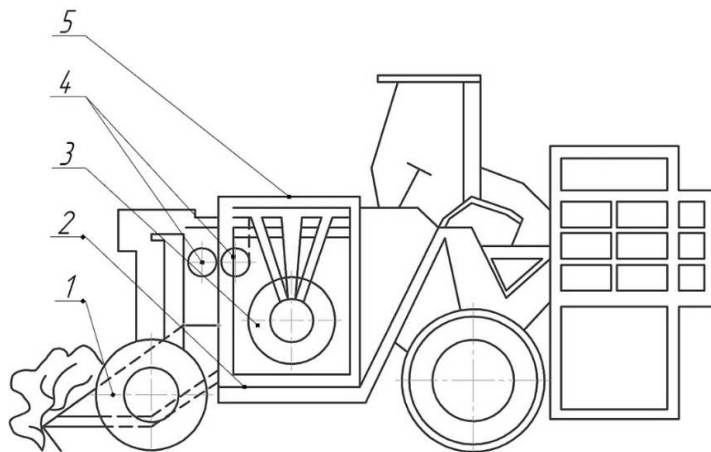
Установка формирователя на комбайне: 1 – формирователь; 2 – поперечный транспортер; 3 – вибратор; 4 – блоки; 5 – рама улавливателя
